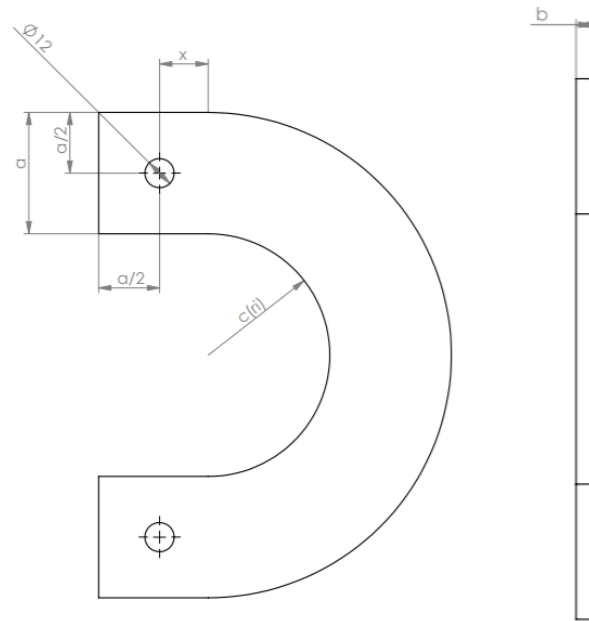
Geometria i dimensions de la peça d'estudi en mm
